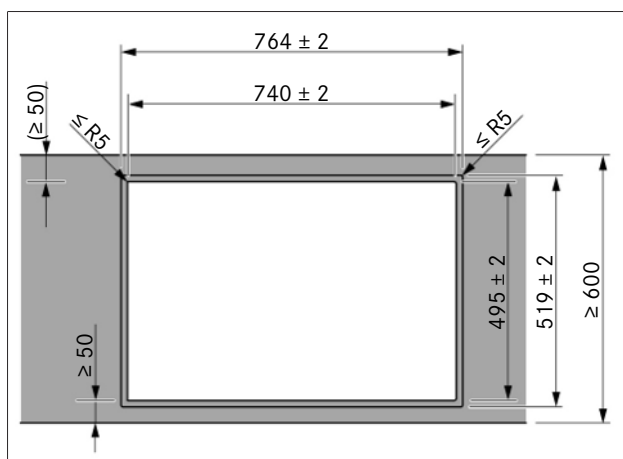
Dimensioni intaglio per montaggio a filo
